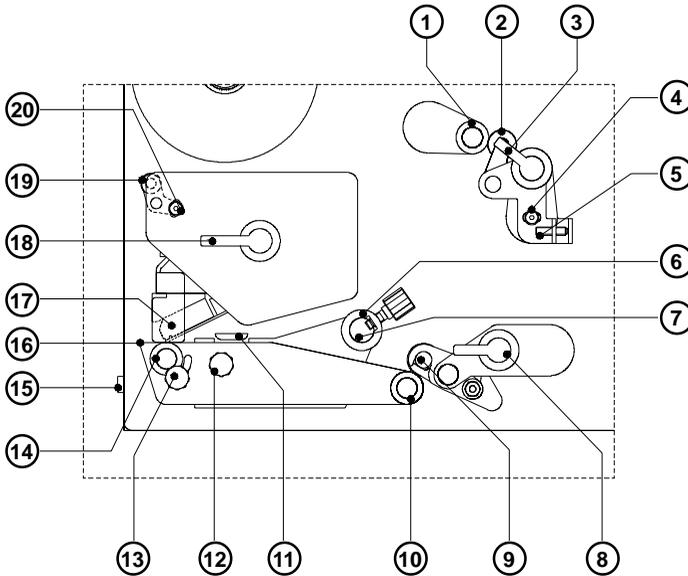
Detailsicht Druckmechanik Hermes 4N/5N
